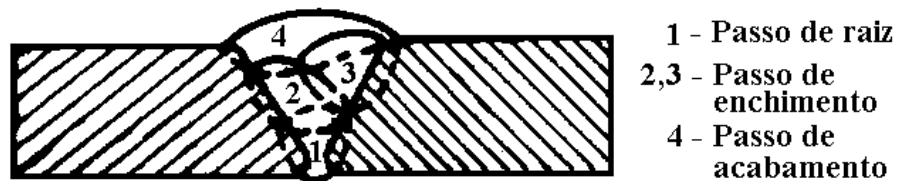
Soldagem de topo ou soldagem múltiplos passes.
